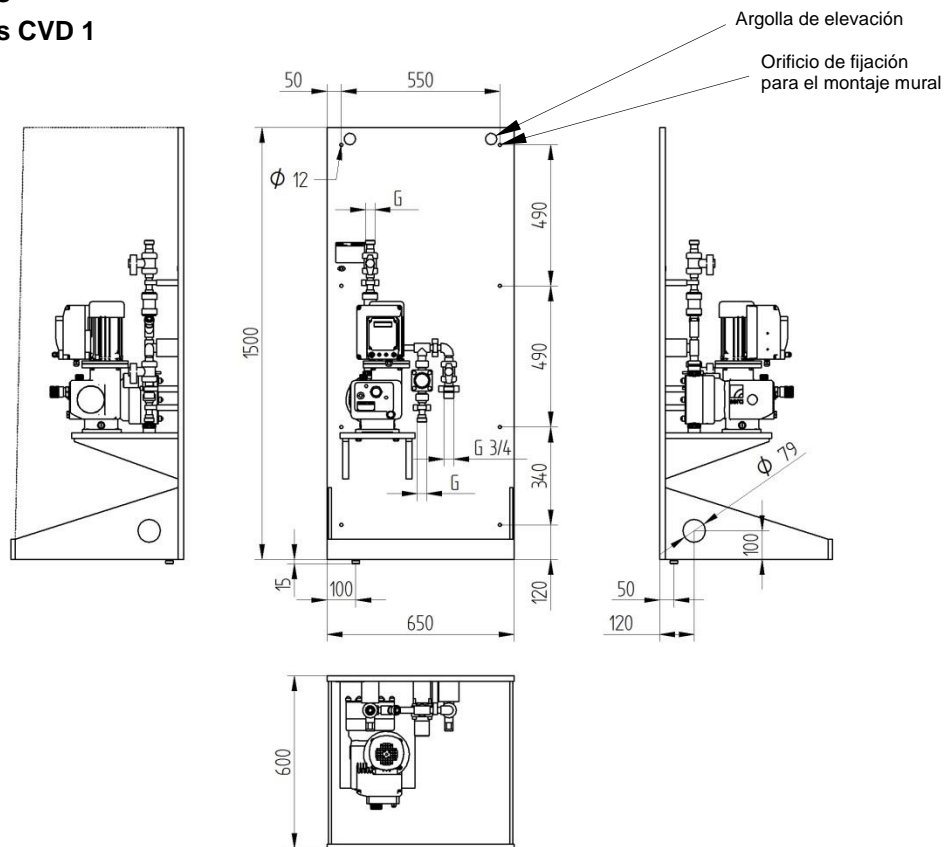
Dimensiones CVD1 (montaje en pared)
